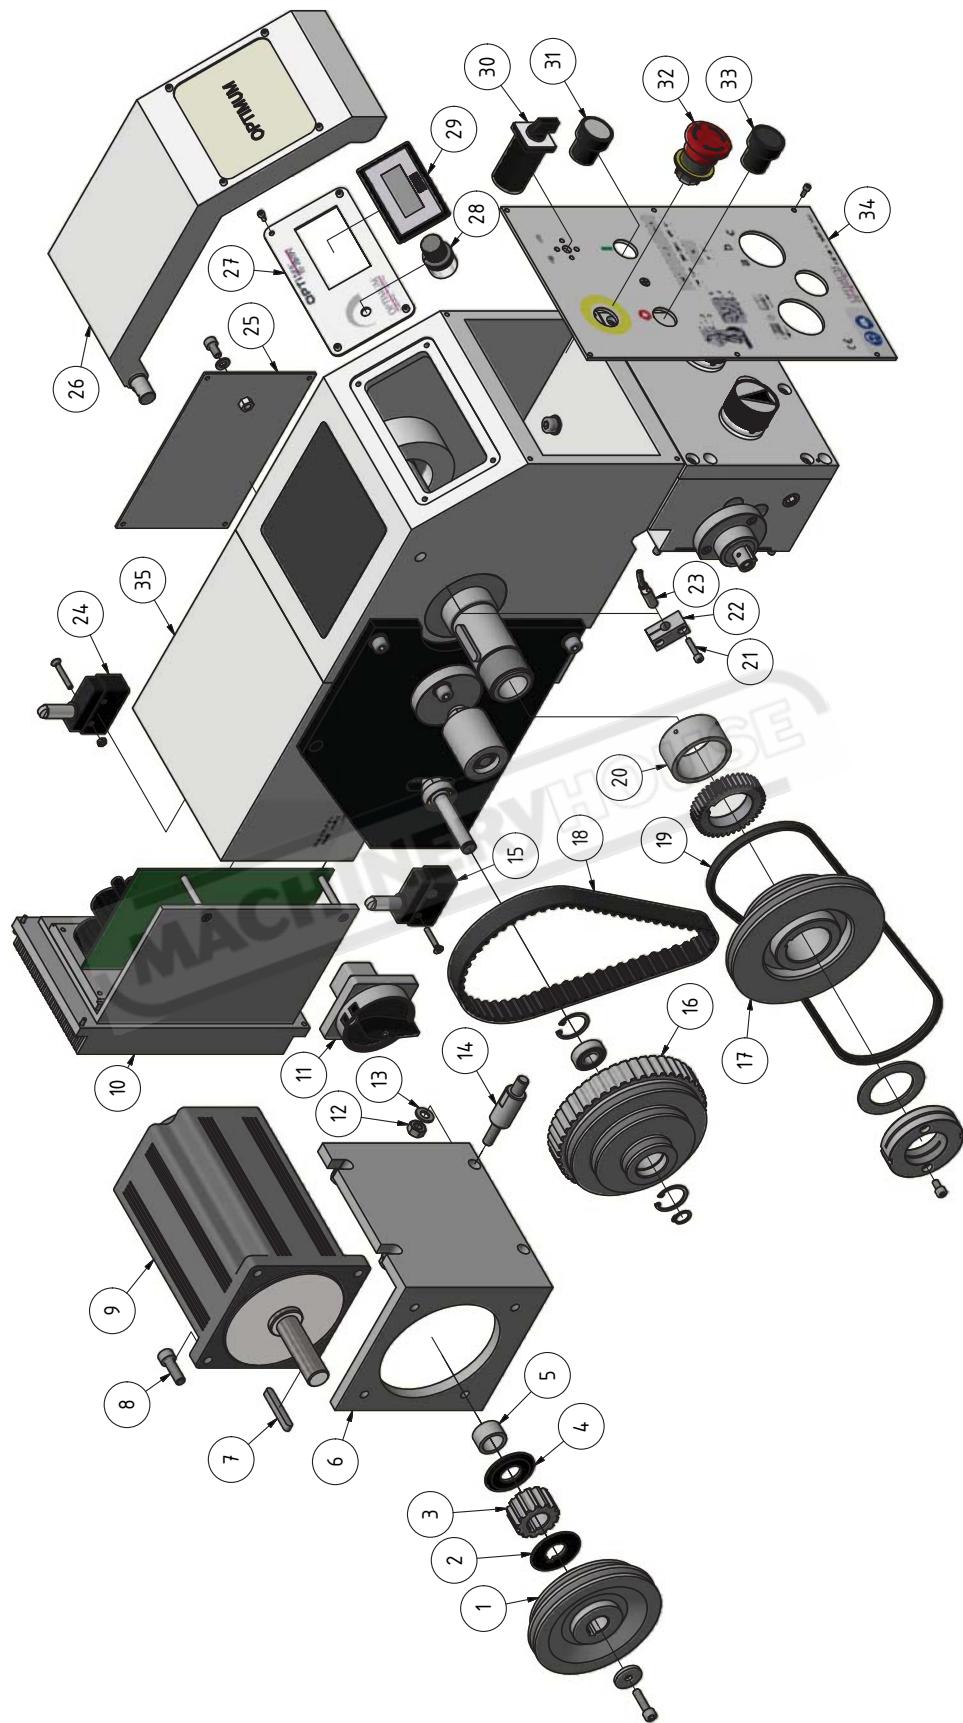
Spindelstock - Headstock TU 2807 V
